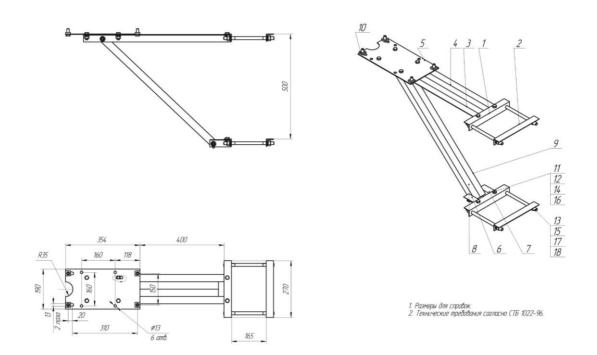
Габаритные размеры и сборочный чертеж монтажного комплекта трансформатора напряжения реклоузера CET-RV-10.
